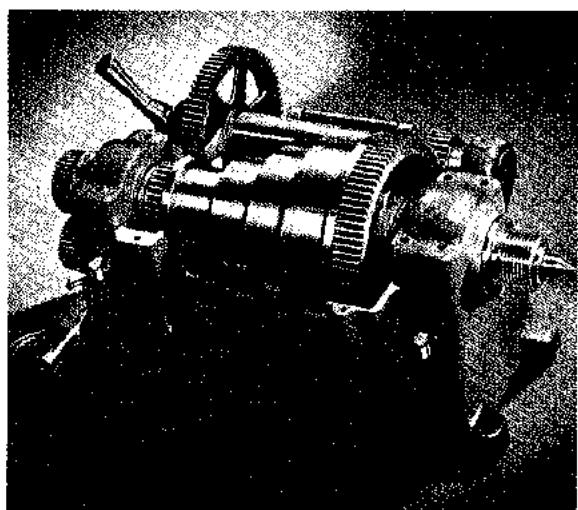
Cabezal con cono de poleas mostrando la disposición de los engranajes de cambio (South Bend Lathe Works).
